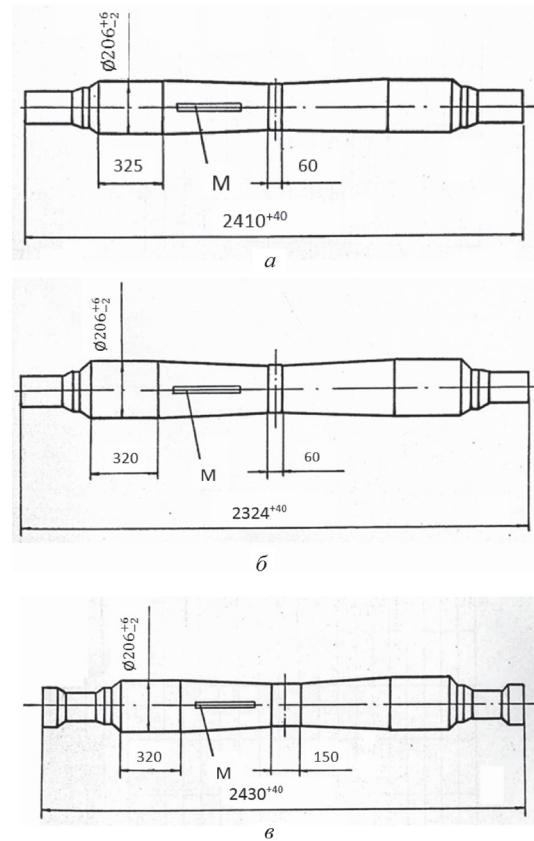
Профили сплошных катаных вагонных осей: а, б – для подшипников качения; в – с фланцем для подшипников скольжения; М – место маркировки
